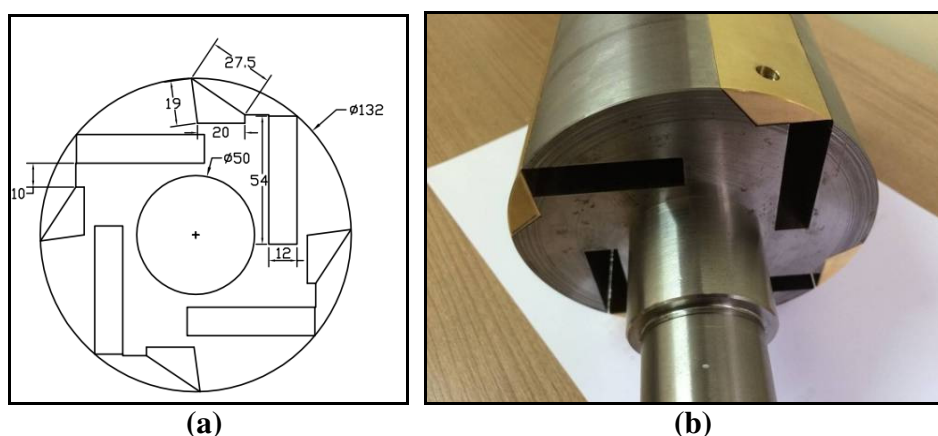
Rotor com ímãs embutidos – (a) Desenho esquemático – (b) rotor montado [30]
